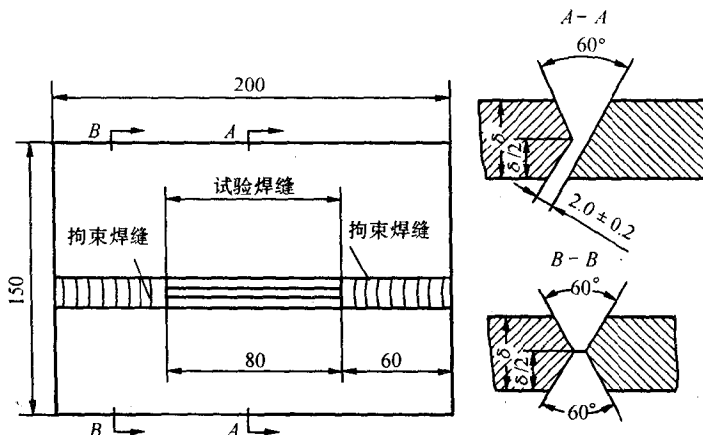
斜 Y 形坡口焊接裂纹试验试件的形状和尺寸
